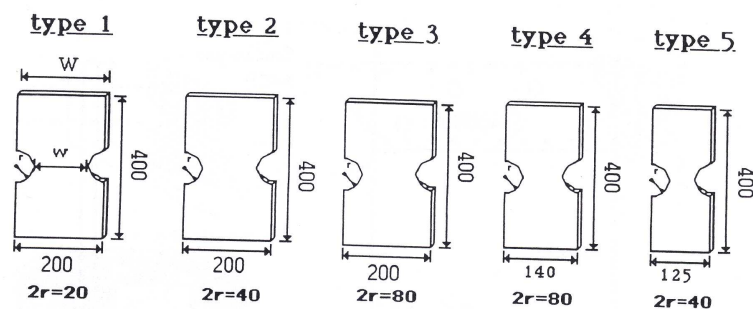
Test avec éprouvettes entaillées [Priadi, 1993].
